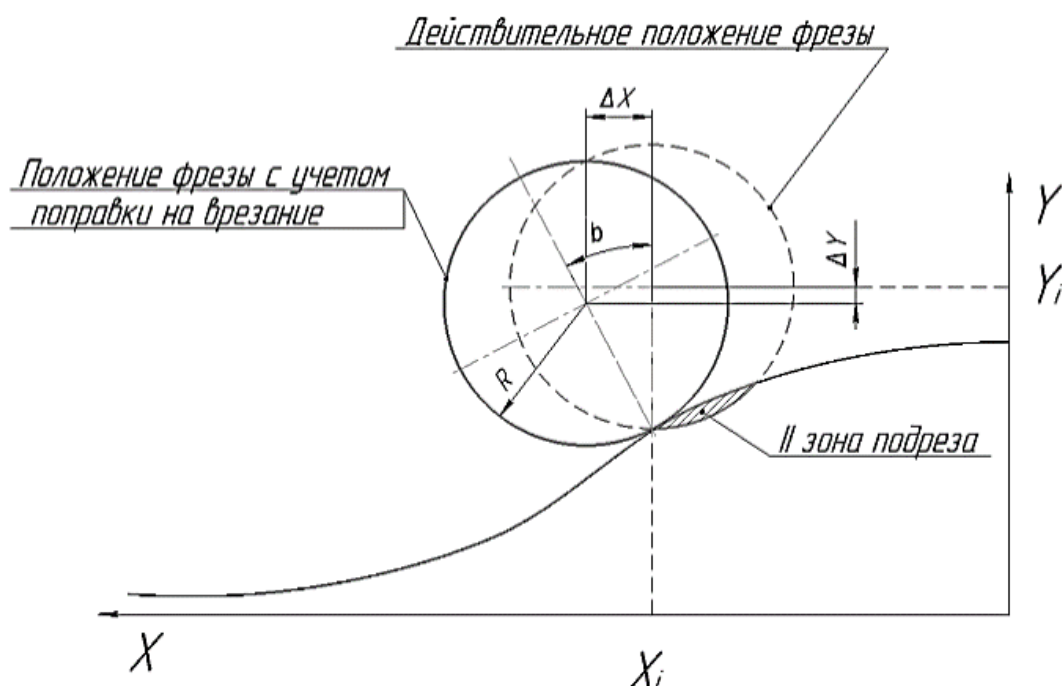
Графическое изображение относительного положения инструмента и заготовки ротора во время обработки в плоскости, расположенной вдоль оси заготовки
